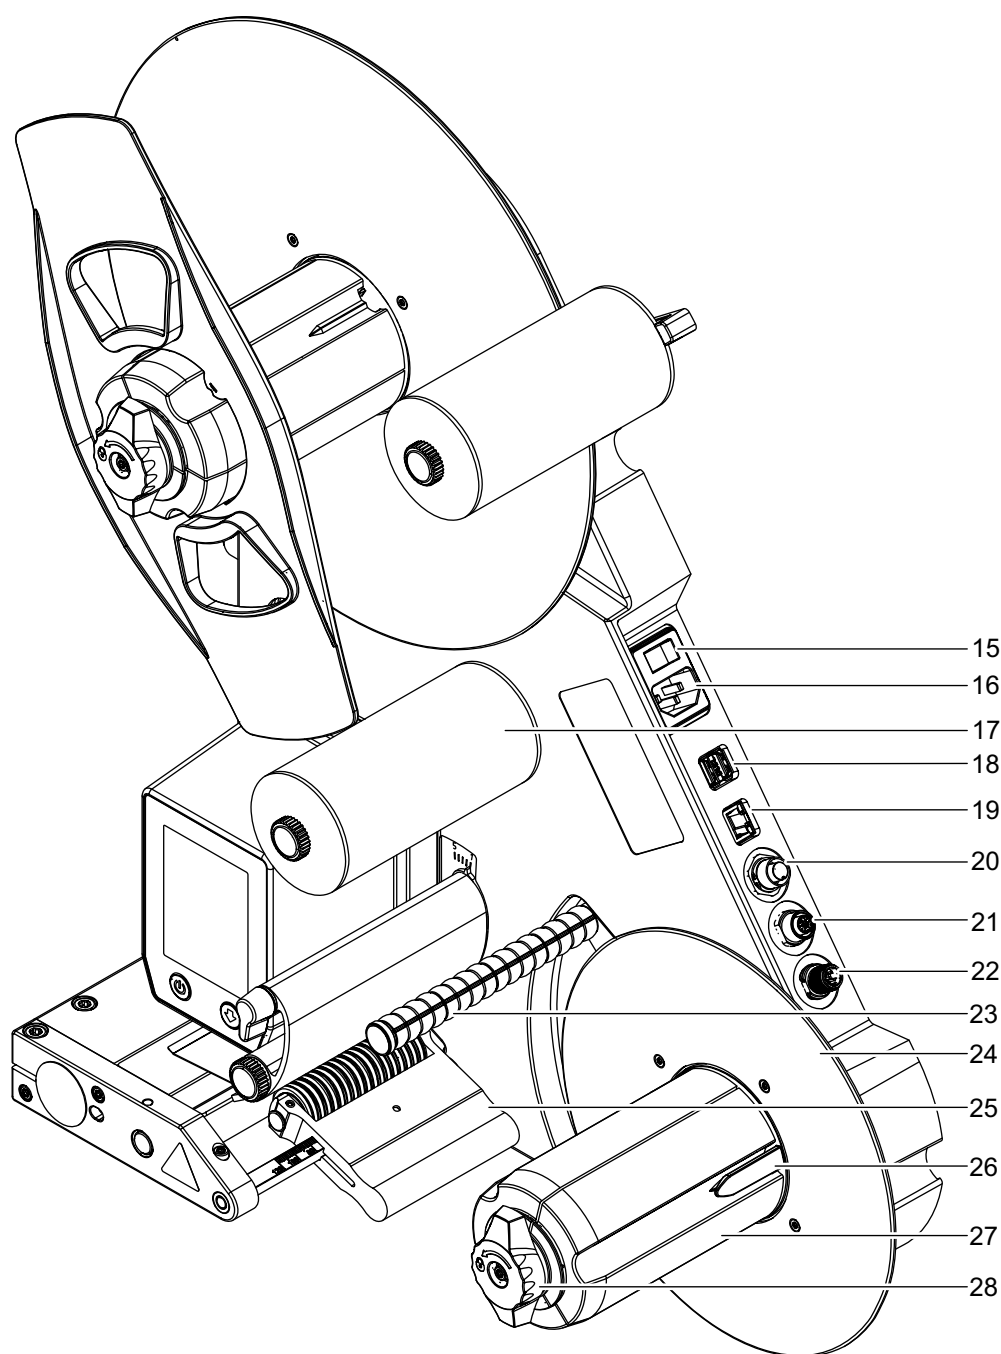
Vue d'ensemble étiqueteuse, vue côté droit
